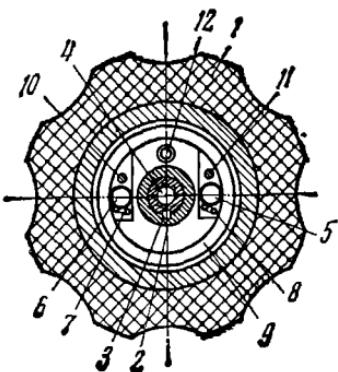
Разрез рукоятки механизма установки кадра в рамку кинопроектора типа КПТ
